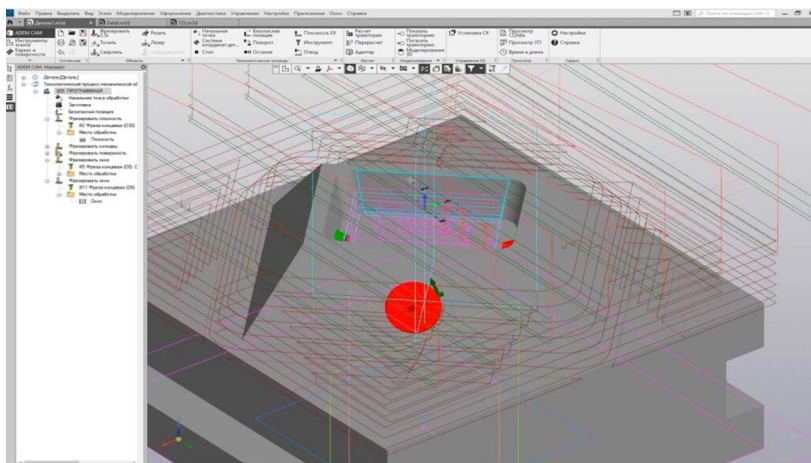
Модуль ЧПУ. Фрезеровка [9]
